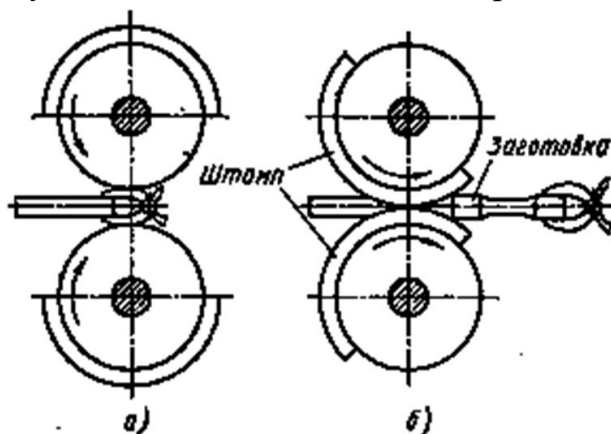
Схема вальцовки на ковочных вальцах: а – исходное положение; б – вальцовка
